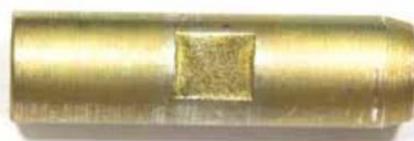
Втулка: внутренняя резьба с левой стороны – левая,
